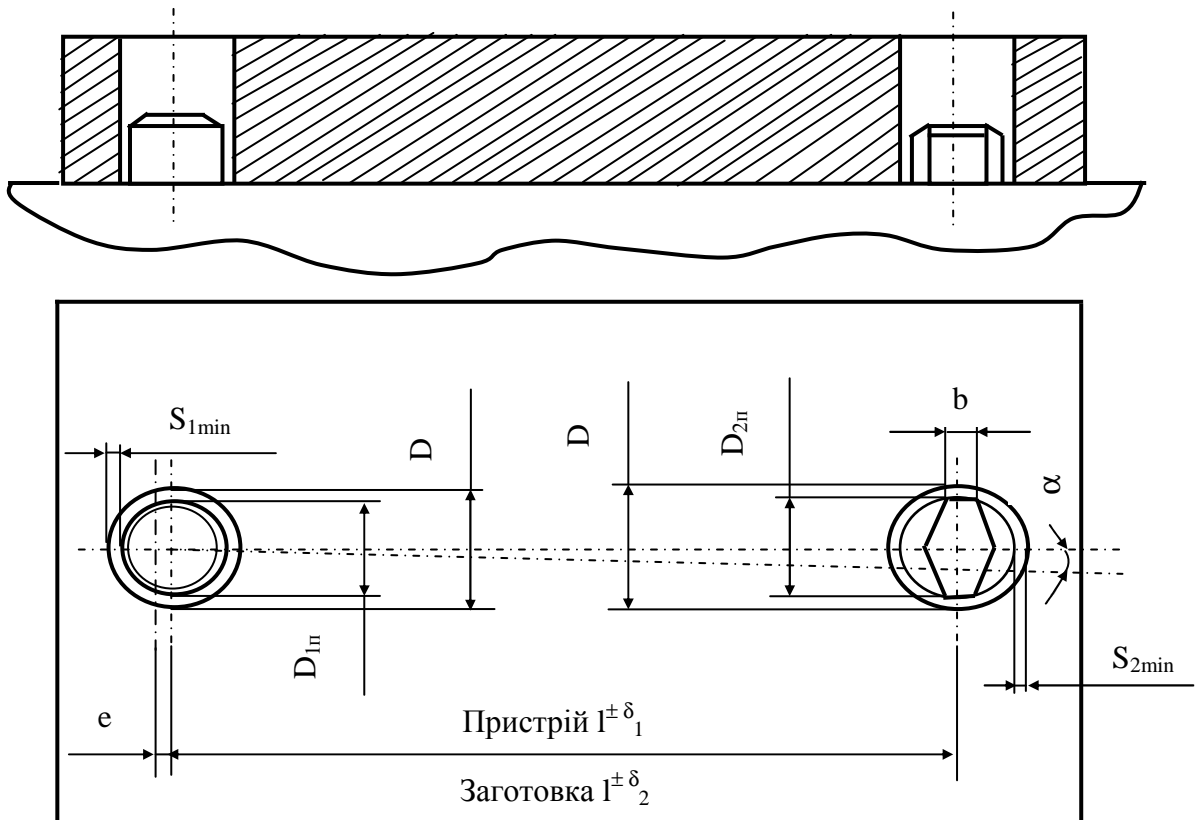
Базування заготовки двома отворами на циліндричний та зрізаний палець
